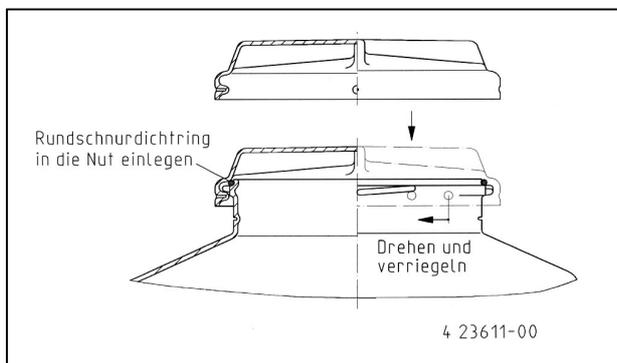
Einbau Deckel Baufix 200 Überflur (23611)
